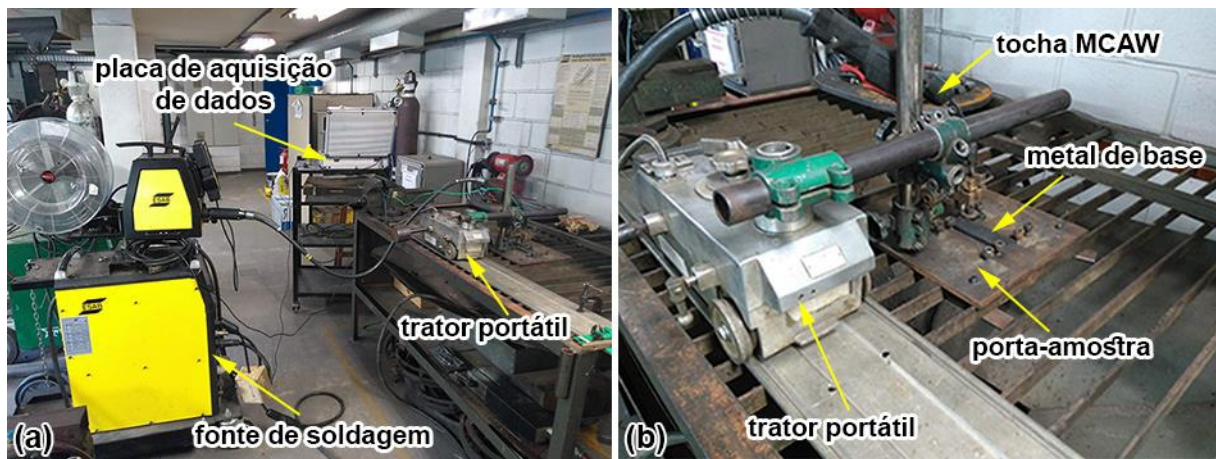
(a) Fonte inversora de soldagem. (b)Esquema de soldagem dos arames tubulares.
